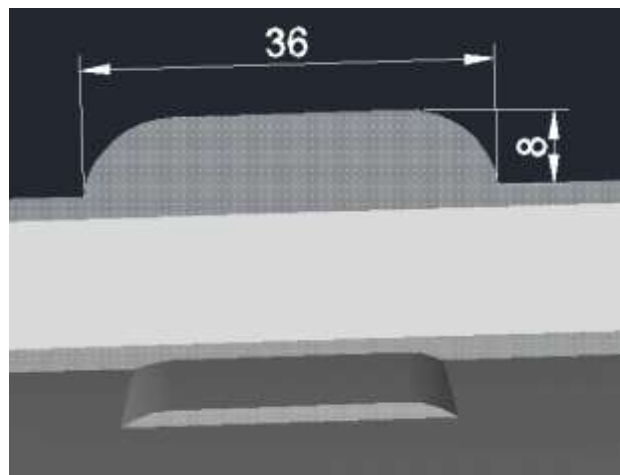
Detalhe do corte do apoio de maior dimensão da telha GePET.
